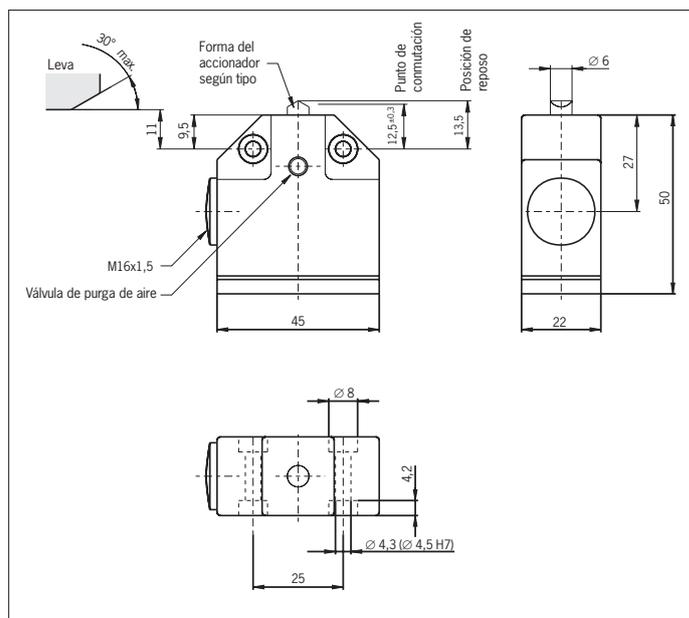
Plano de dimensiones SN01... con entrada de cable
